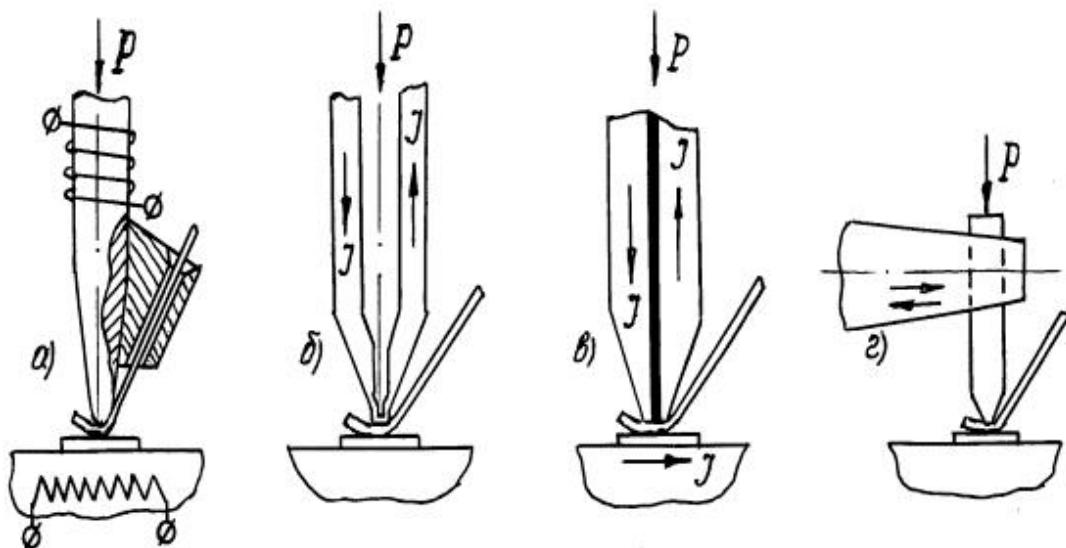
Виды микросварки. Разновидности сварочного инструмента а) – ТКС; б) – СКИН; в) – ЭКОС; г) – УЗС
